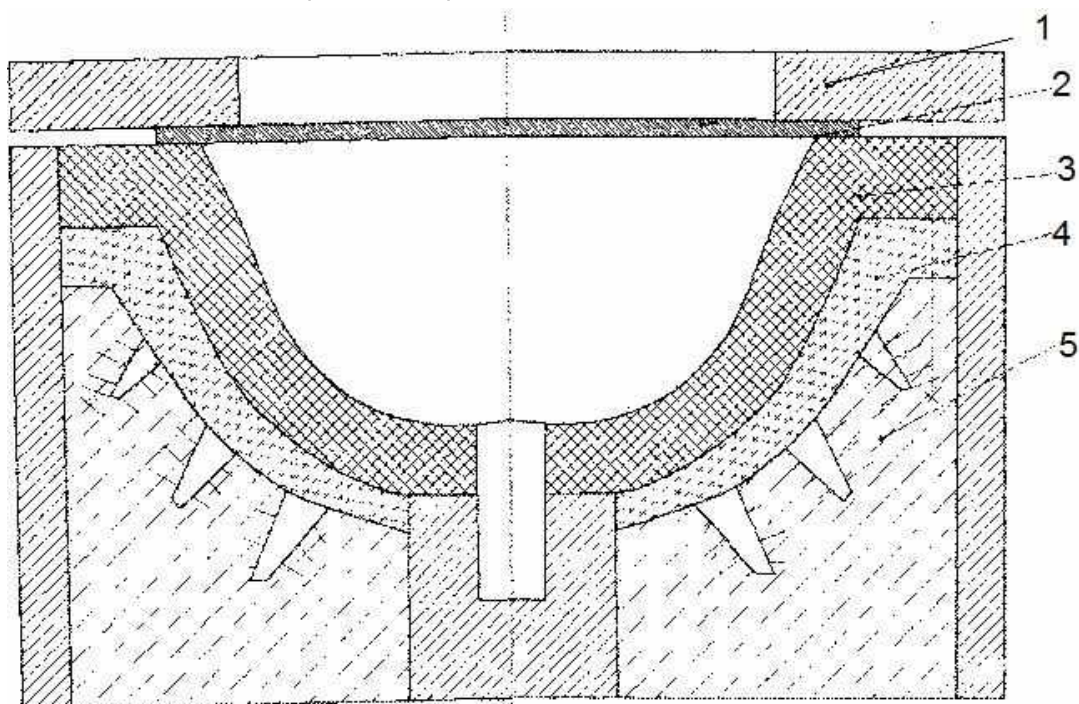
Штмп із зварною матрицею, фанерованою епоксидною смолою:
